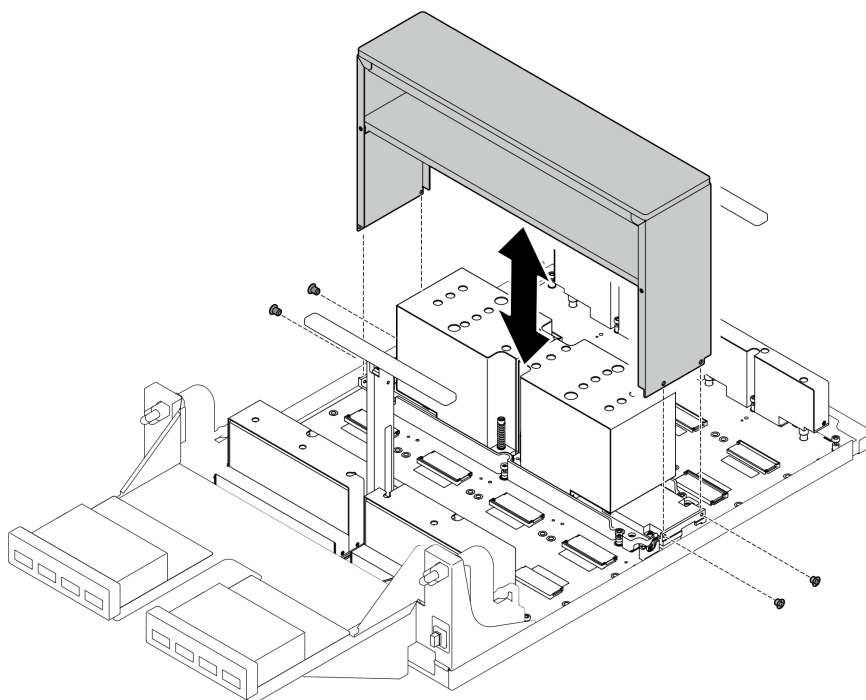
Installation du cache du dissipateur thermique NVSwitch
